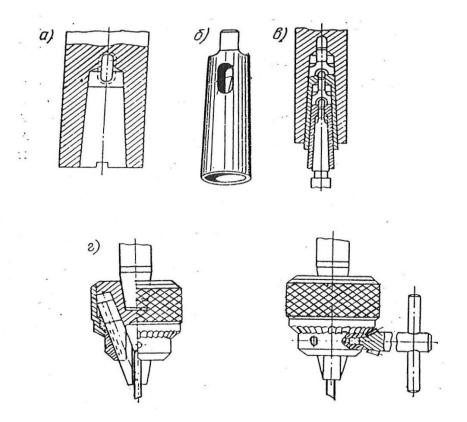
Приспособления, применяемые на сверлильных станках: а — разрез шпинделя станка; б — переходная втулка (конус Морзе); в — разрез шпинделя станка с переходными втулками; г — сверлильный патрон
